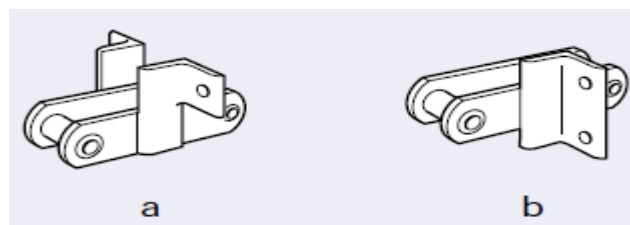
Accesorios tipo F. a) F1, accesorios soldados a placas de unión en uno o ambos lados de la cadena según sea necesario y b) F2, soldadas a placas de unión en uno o ambos lados de la cadena según sea necesario.
